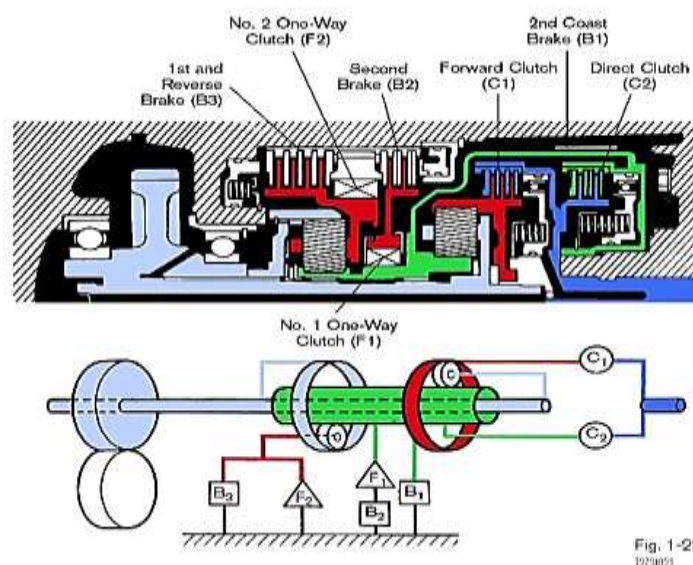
Konstruksi Poros *Planetary Gear Unit* pada Transmisi Otomatis Seri A130
